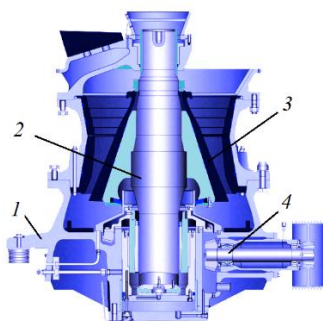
Схема конусной дробилки: 1 – станина; 2 – основной вал; 3 – броня; 4 – приводной вал
